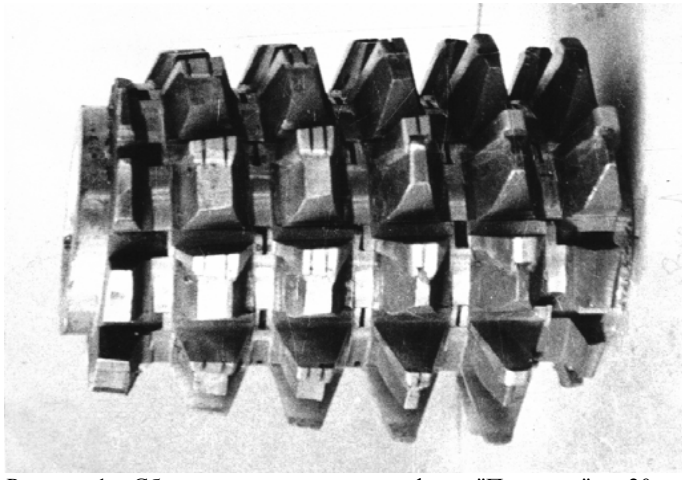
Сборно-сварная червячная фреза "Прогресс" $m=20$ мм с сборным конусом и стружкоразделительными канавками
